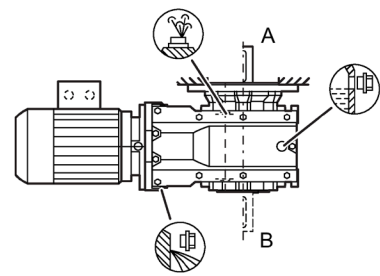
Einbaulagen für Kegelradgetriebe B.F Flanschführung und B.Z mit Gehäuseflansch, Baugrößen 39 - 49
